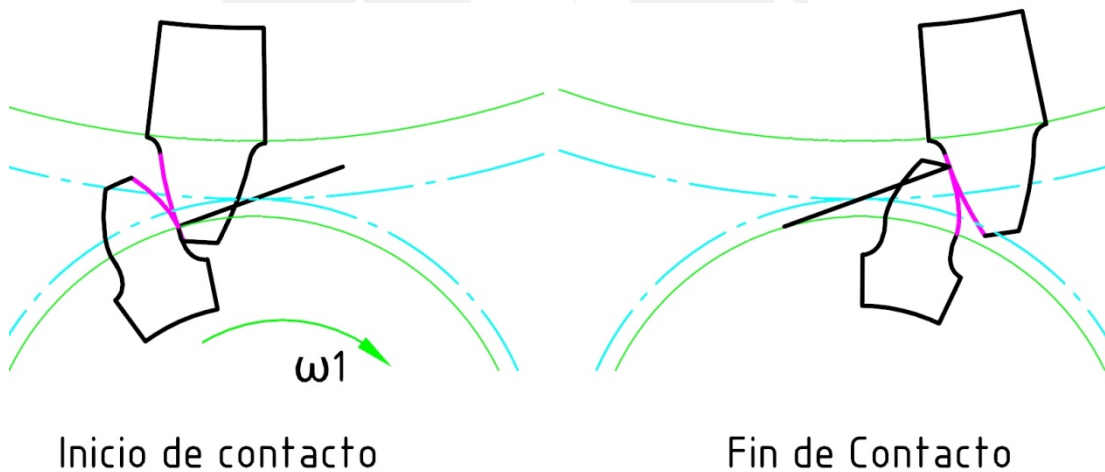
Inicio y fin de contacto de un par de engranajes
